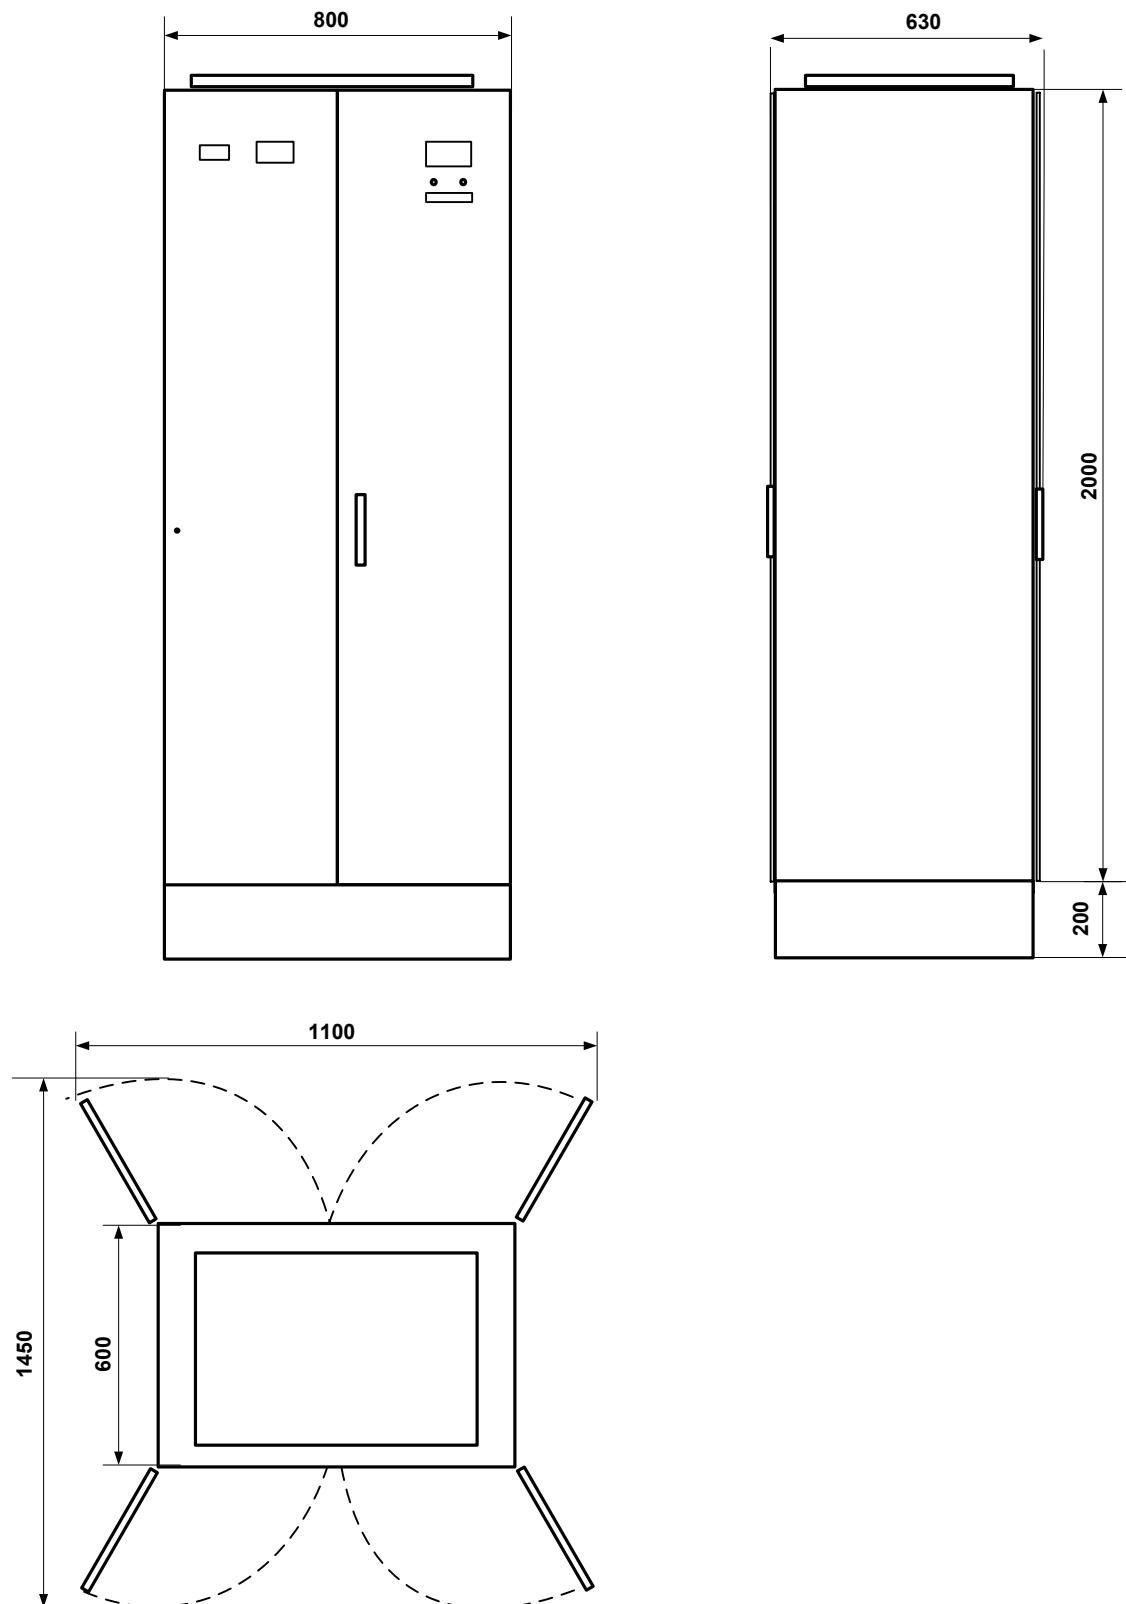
Габаритный чертёж напольной стойки БРКУ
